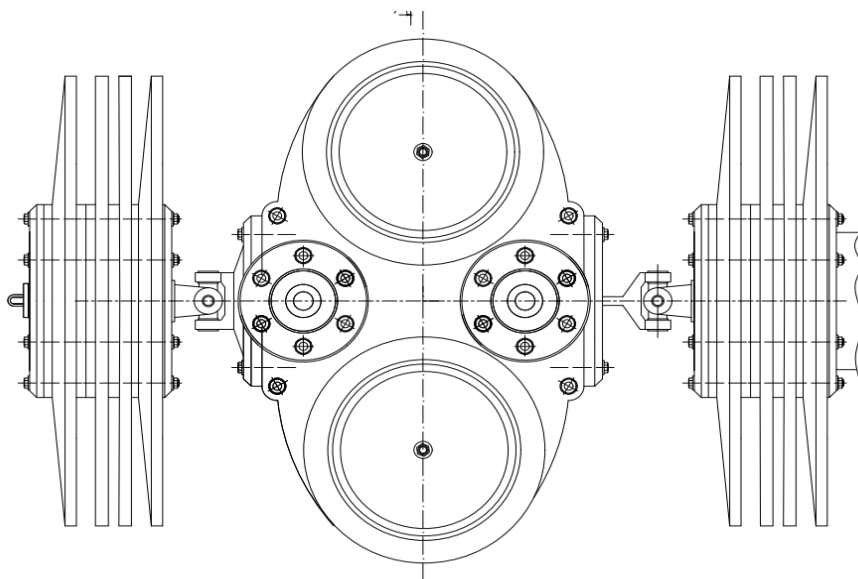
Зовнішній вид приводної частини діагностичного внутрішньотрубного пристрою
